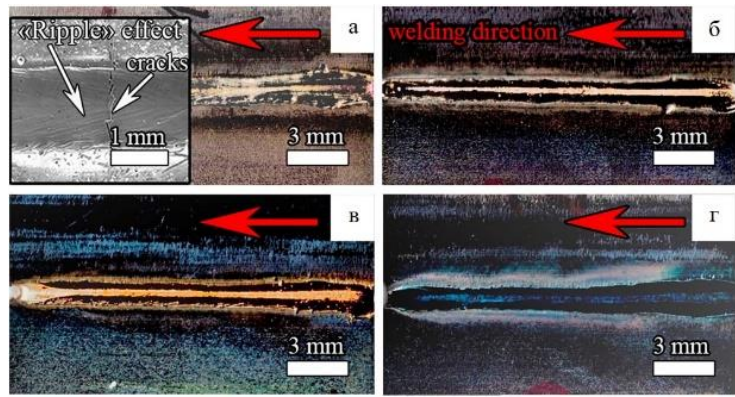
Внешний вид сварных швов, полученных при: а) комнатной температуре; б) предварительный нагрев до 400 °С; в) 600 °С; г) 800 °С. Красные стрелки указывают направление сварки лазерным лучом
